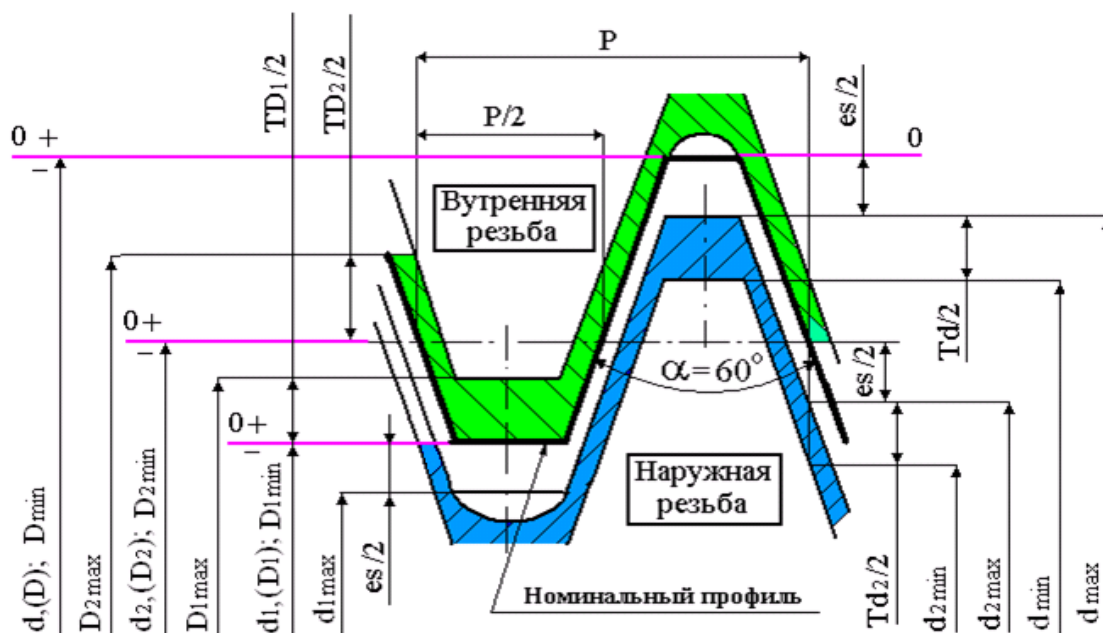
Расположение полей допусков метрической резьбы при посадке с зазором
